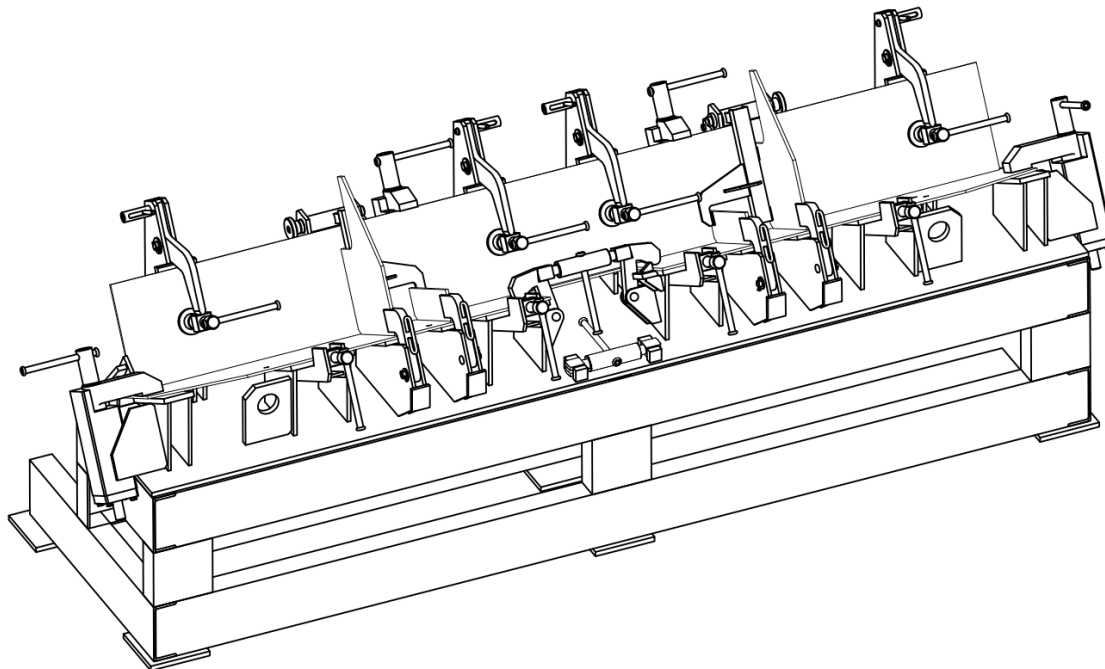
Модель стенда сборки балки концевой (оснащен ручными прижимными устройствами)
